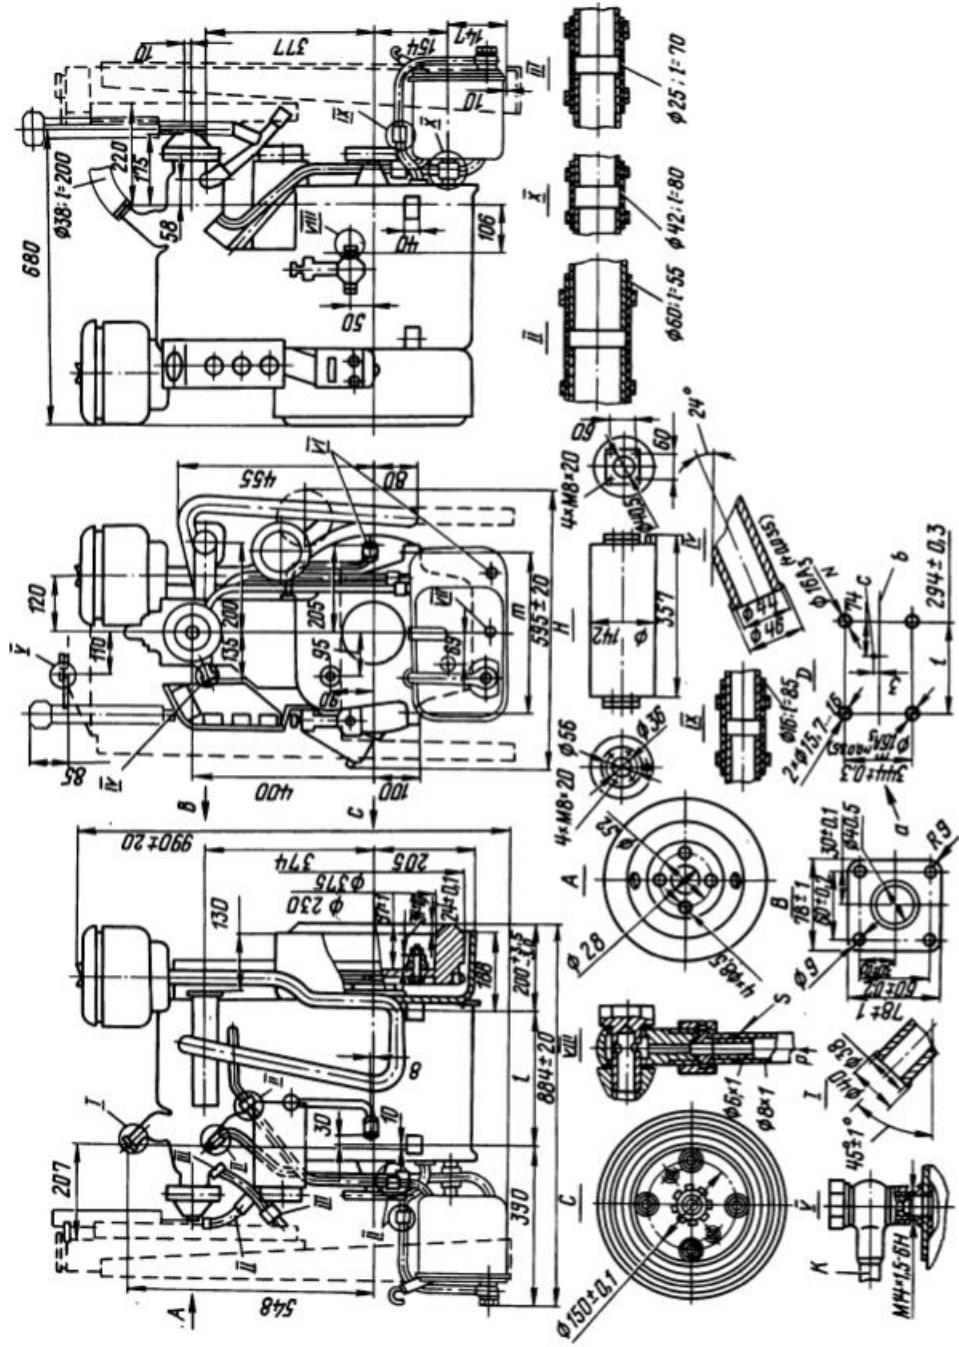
Габаритный чертеж дизеля 2Д 8,5/11 (ЗР2-С):
